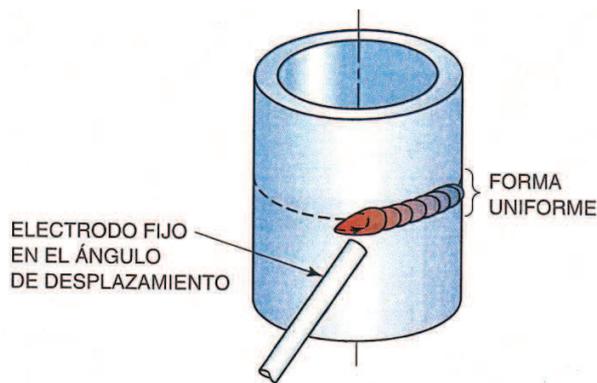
POSICIÓN DE SOLDADURA DE TUBO 2G
